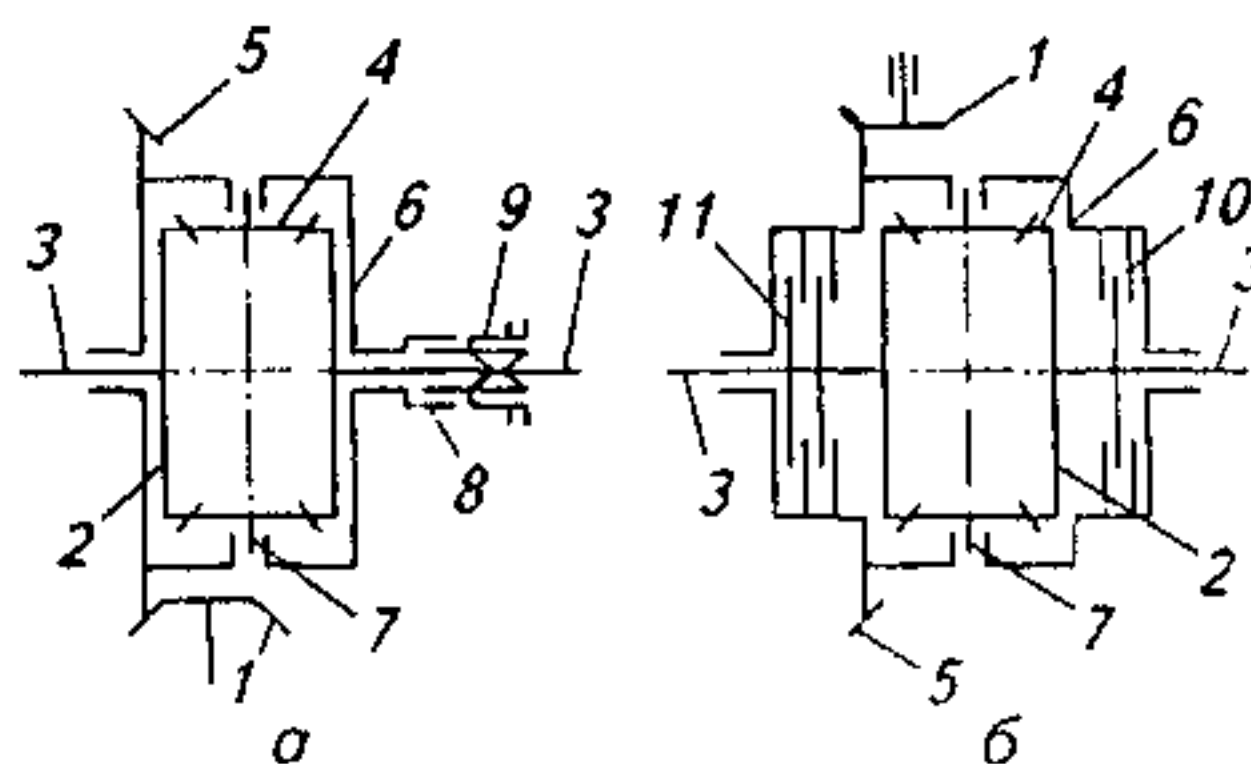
Схема шестеренного дифференциала: а — блокируемого; б — самоблокирующегося; 1 — ведущая шестерня главной передачи; 2 — полуосевая шестерня; 3 — полуоси; 4 — сателлит; 5 — ведомая шестерня главной передачи; 6 — корпус дифференциала; 7 — крестовина; 8 — зубцы корпуса; 9 — зубчатая муфта; 10, 11 — соответственно ведущие и ведомые диски
